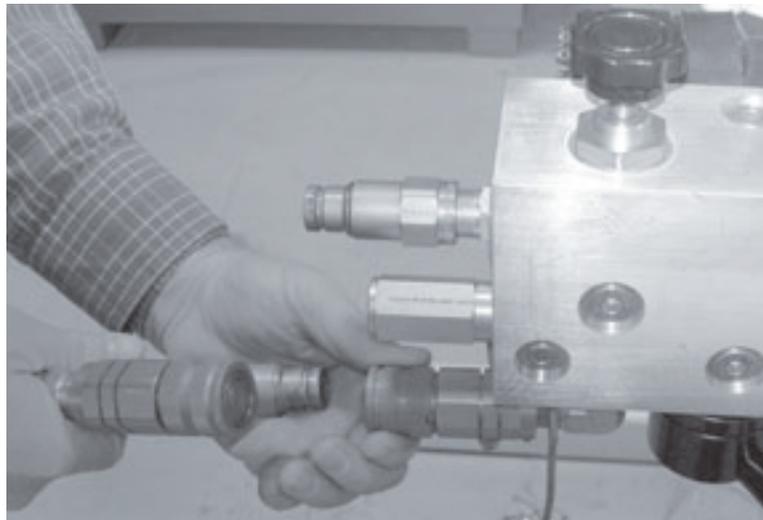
Scollegare l'alimentazione idraulica rimuovendo i tubi idraulici dai raccordi sul collettore.
